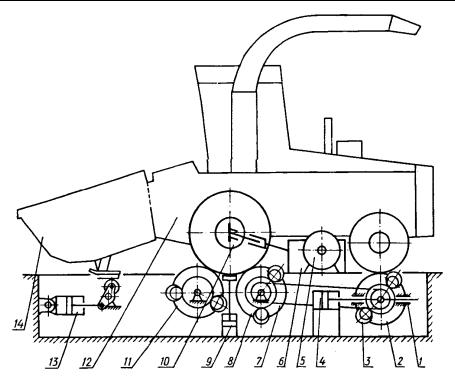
Схема стенда для комплексных испытаний кормоуборочных комбайнов: 1 — направляющая; 2 — задний барабан; 3 — препятствие; 4 — гидроцилиндр; 5 — тормоз; 6 — редуктор; 7 — цепная передача; 8, 11 — передние барабаны; 9 — подъемник, 10 — карданная передача; 12 — самоходный измельчитель; 13 — гидроцилиндр нагружения; 14 — жатка
